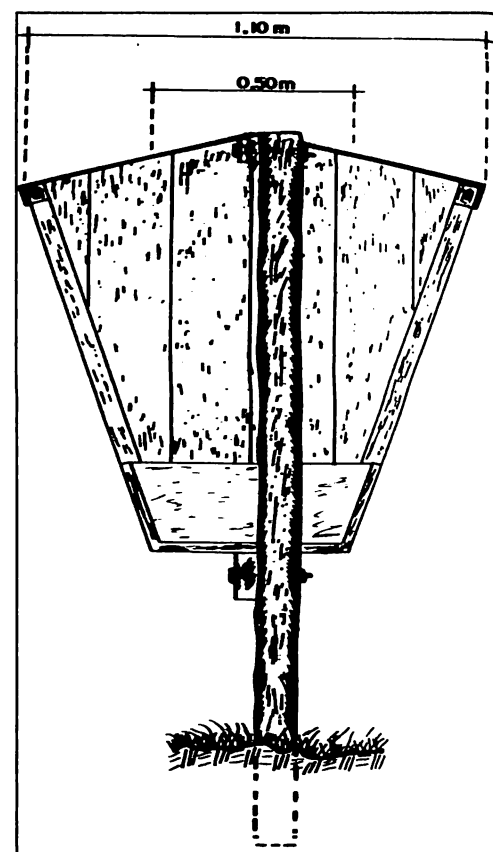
Vista lateral do mini-saleiro automático-unidade (MSA-1).
